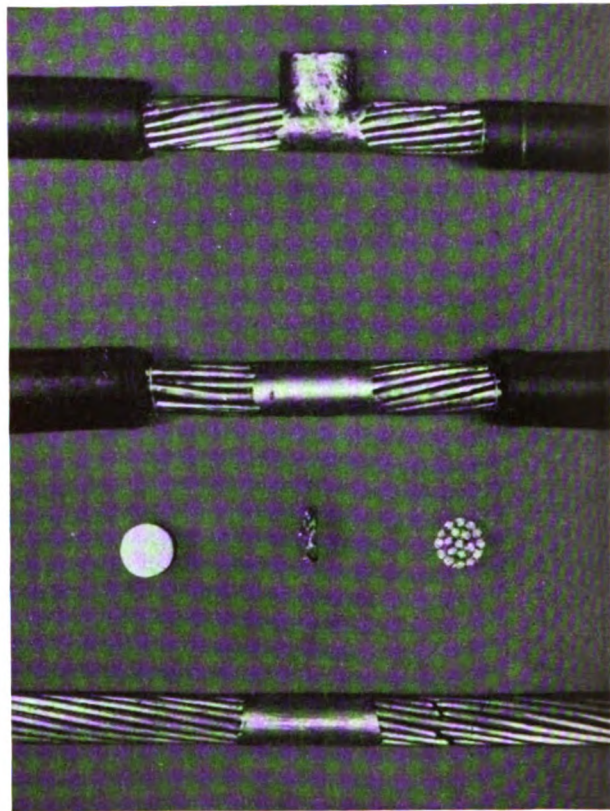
Schweißverbindungen nach dem Gießverfahren.
